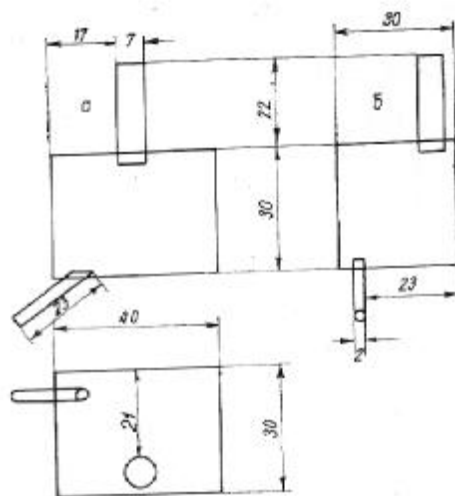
Бачок для пального: а) вигляд збоку; б) вигляд спереду.
